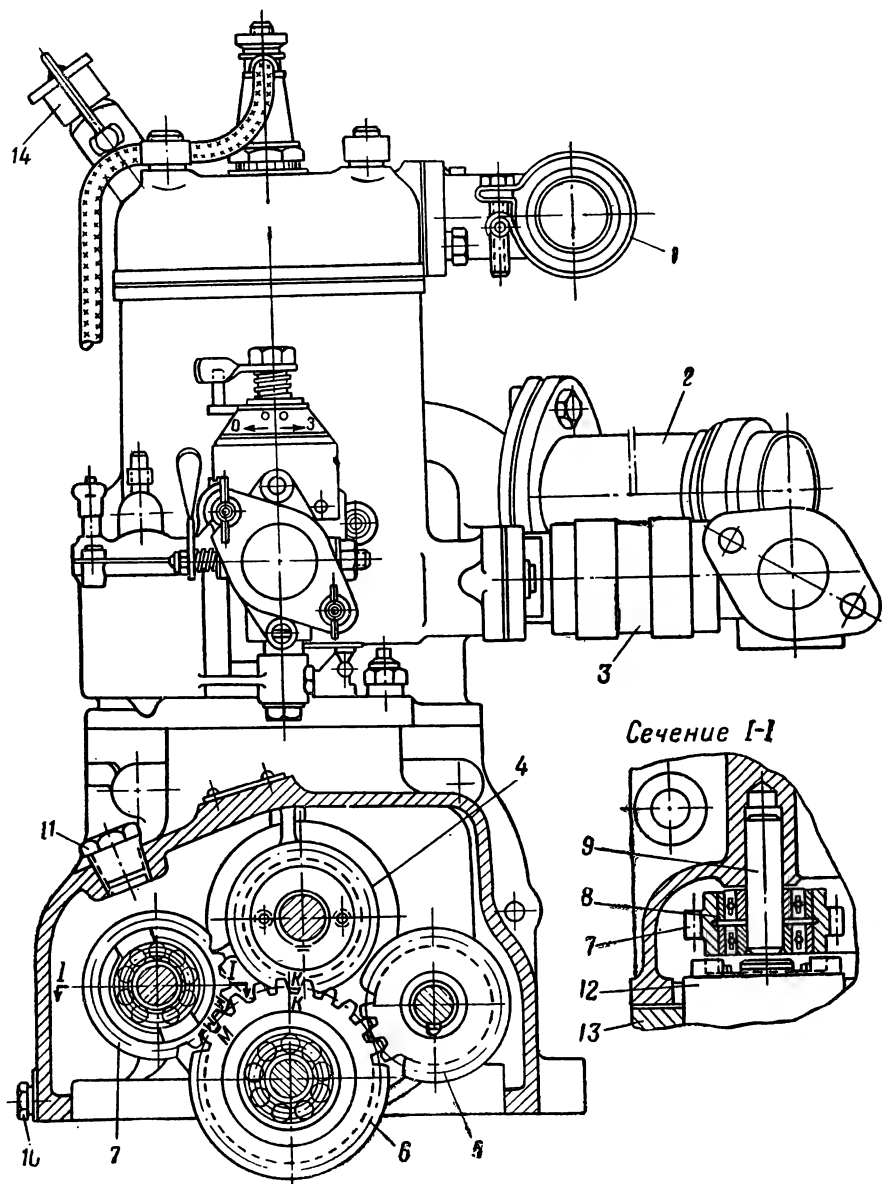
Пусковой двигатель (вид спереди и разрез по шестерням распределения).
